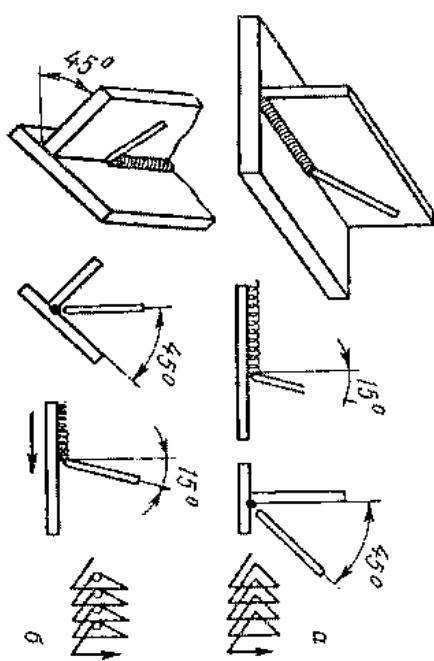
Положение и движение электрода при сварке угловых швов:
